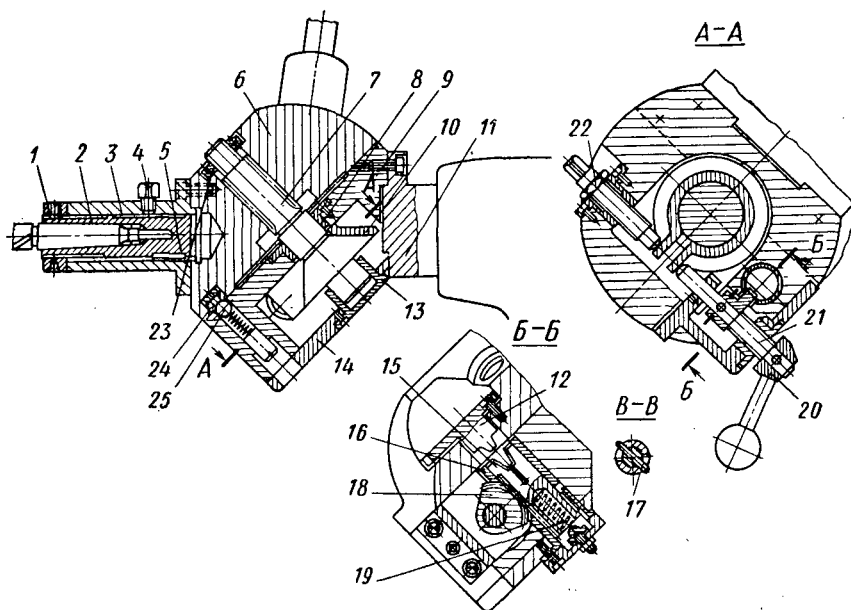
Револьверная головка, устанавливаемая на задней бабке
